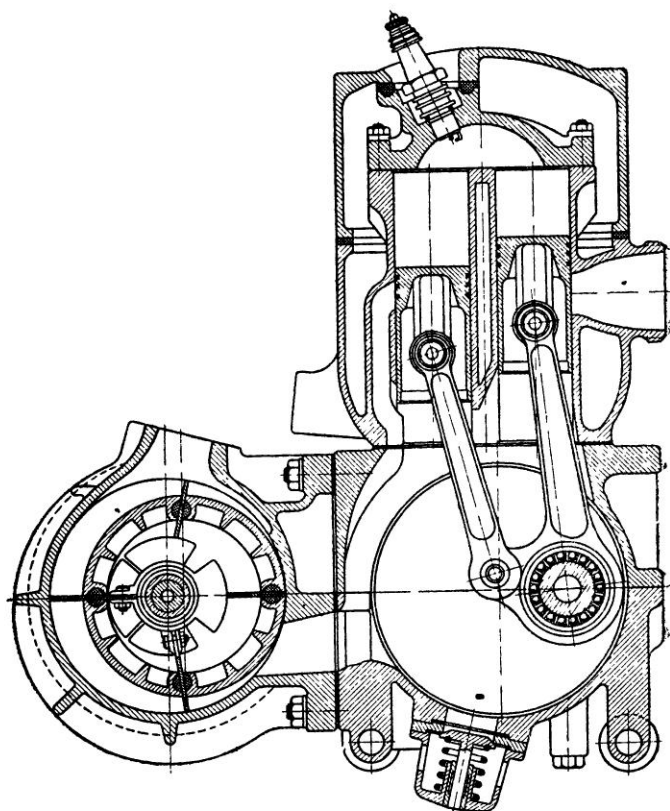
Схема двухтактного двигателя с П-образным расположением цилиндров
